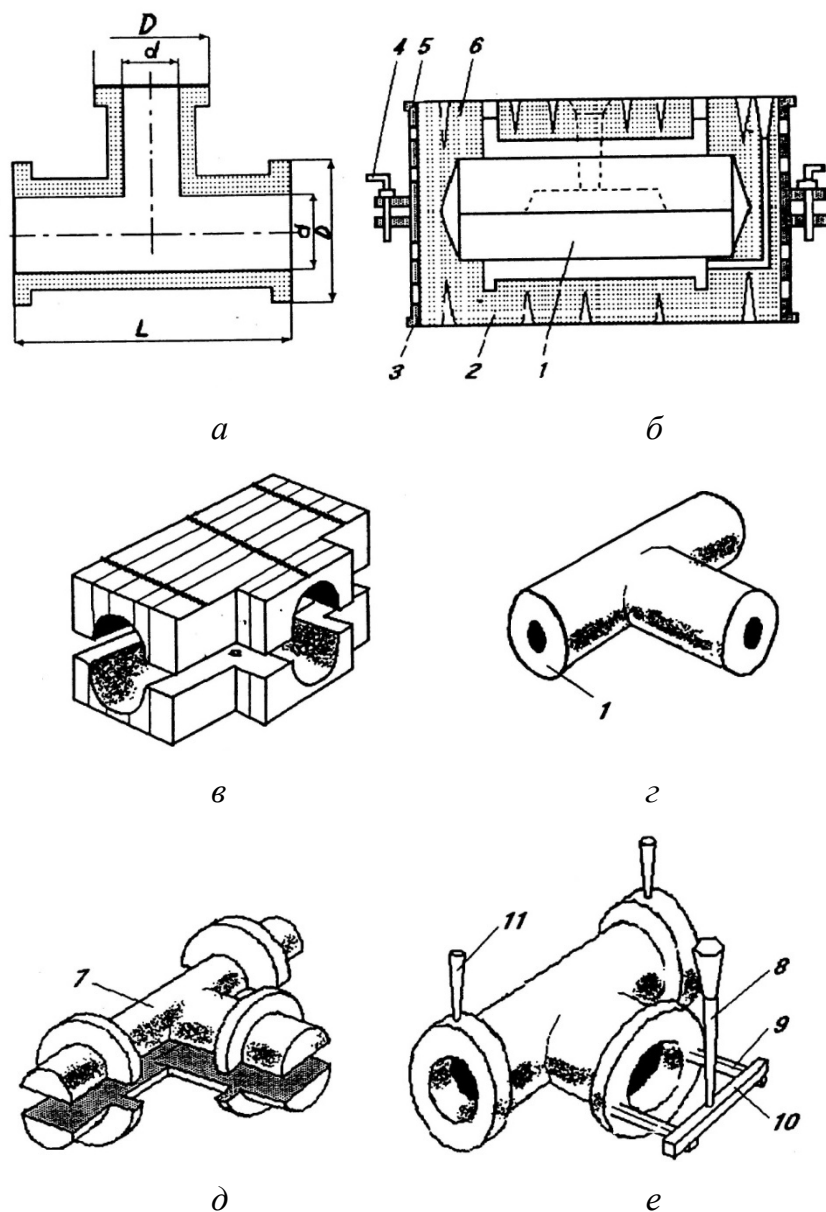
Литейная форма и ее элементы: а – деталь-тройник; б – литейная форма; в – стержневой ящик; г – литейный стержень; д – литейная модель; е – отливка с литниковой системой; 1 – стержень; 2 – нижняя полуформа; 3 – опока; 4 – штырь; 5 – опока; 6 – верхняя полуформа; 7 – модель; 8 – стояк; 9 – питатель; 10 – шлакоуловитель; 11 – выпор
